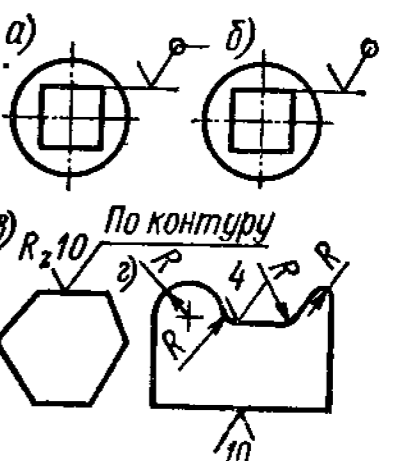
Знаки для обозначения шероховатости на чертежах
